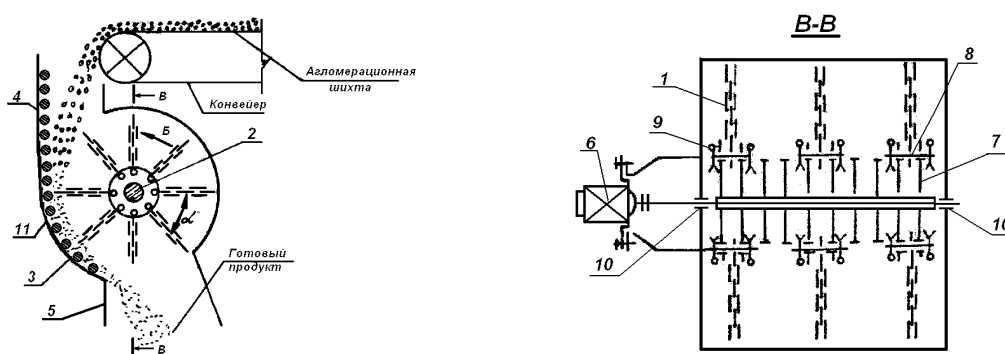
Схема цепного роторного дезинтегратора-смесителя
